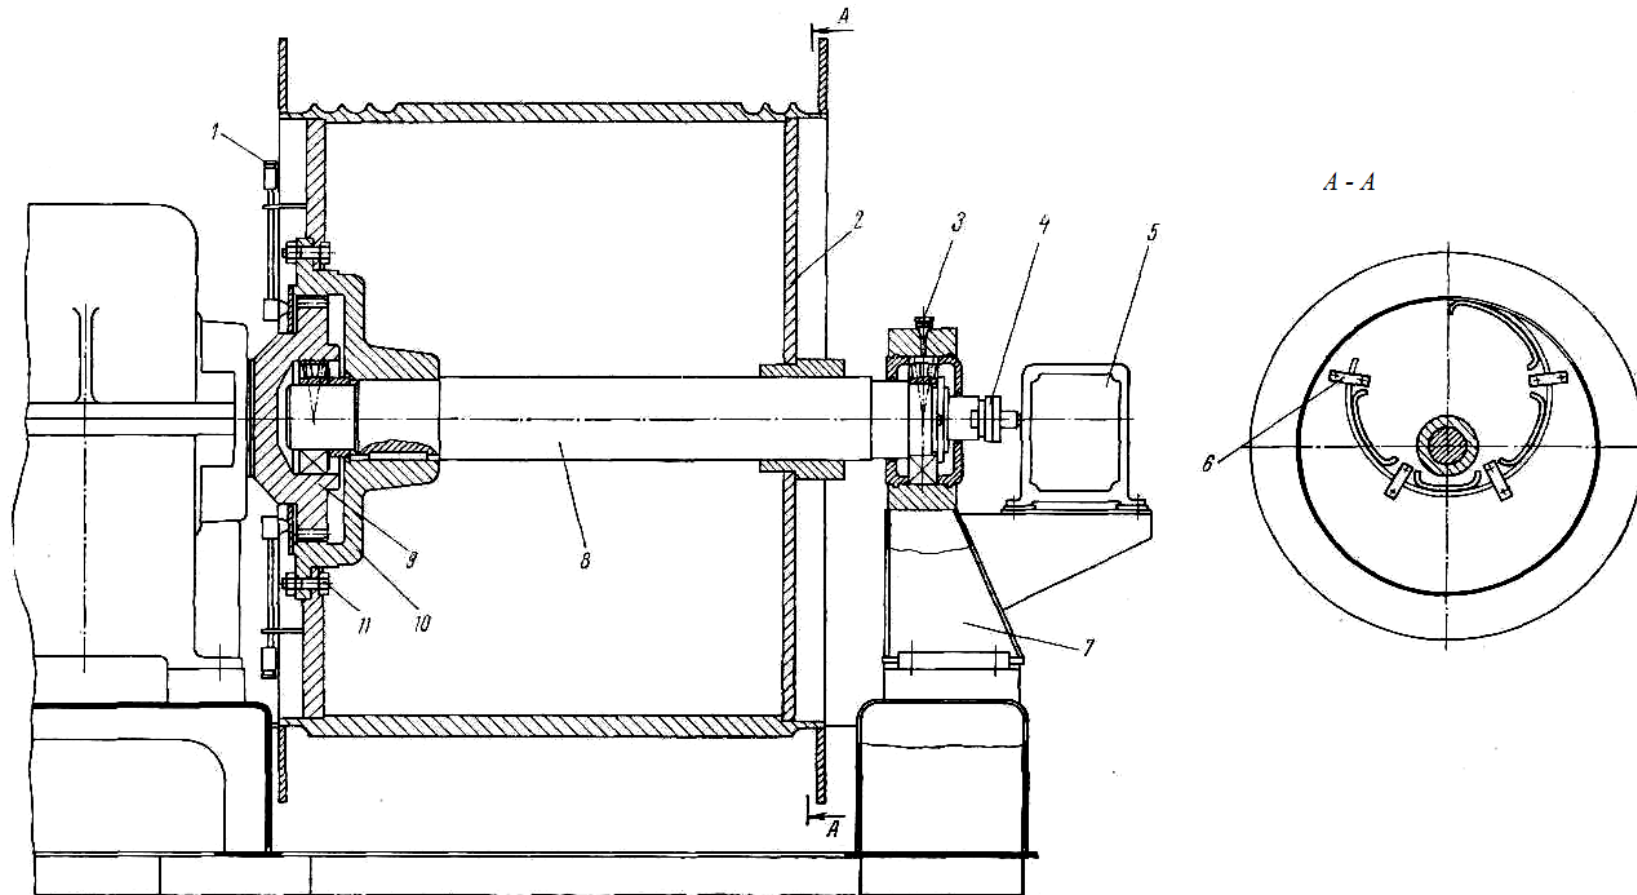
Конструктивное исполнение соединения редуктора и барабана механизма подъема с опорой на ось. На разрезе *A-A* показан вариант крапления каната на щеке барабана: 1,3 — маслѐнка; 2—барабан; 4 — кулачковая муфта Ольдгейма; 5 — конечный выключатель; 6— прижимная планка; 7 — коренной подшипник; 8 — ось; 9 — зубчатый вал редуктора; 10 — зубчатая ступица; 11 — болт
